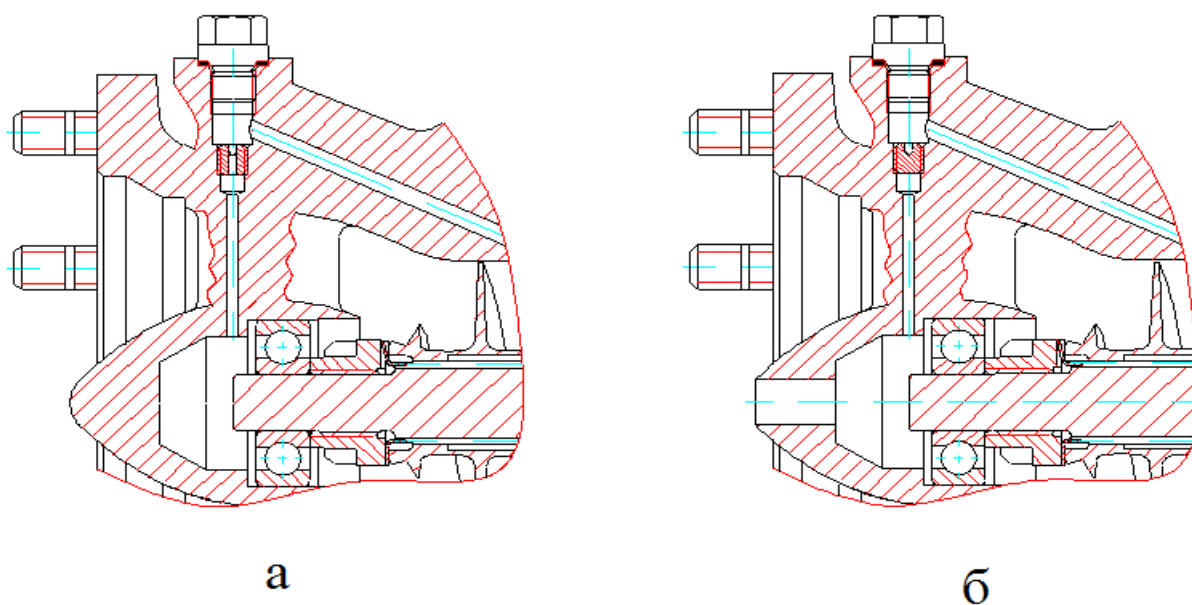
Схема охолодження і змащення неупорного підшипника НО ТНА РРД №2
